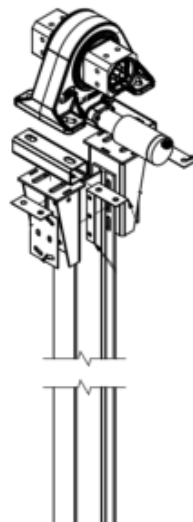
Profilato di fondazione con attacco al corrente longitudinale tramite ghiera metallica
